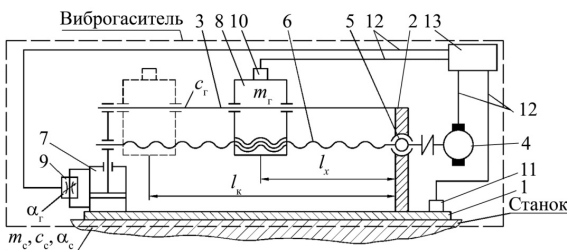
Кинематическая схема динамического виброгасителя: 1) основание; 2) корпус; 3) упругий элемент; 4) шаговый двигатель; 5) шаровая опора; 6) ходовой винт; 7) пневматический демпфер; 8) подвижная масса; 9) регулируемый дроссель; 10) датчик; 11) датчик; 12) информационные каналы; 13) система управления
